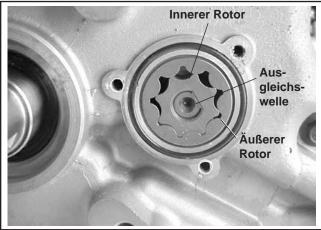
Einbau von Ölpumpengetriebe und O-Ring.
